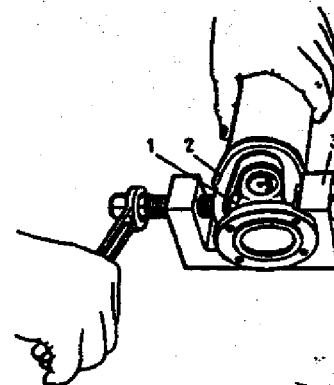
Remoção dos rolamentos: 1 - rolamento de agulhas; 2 - garfo da junta universal; 3 - extrator 67.7823-9522.
